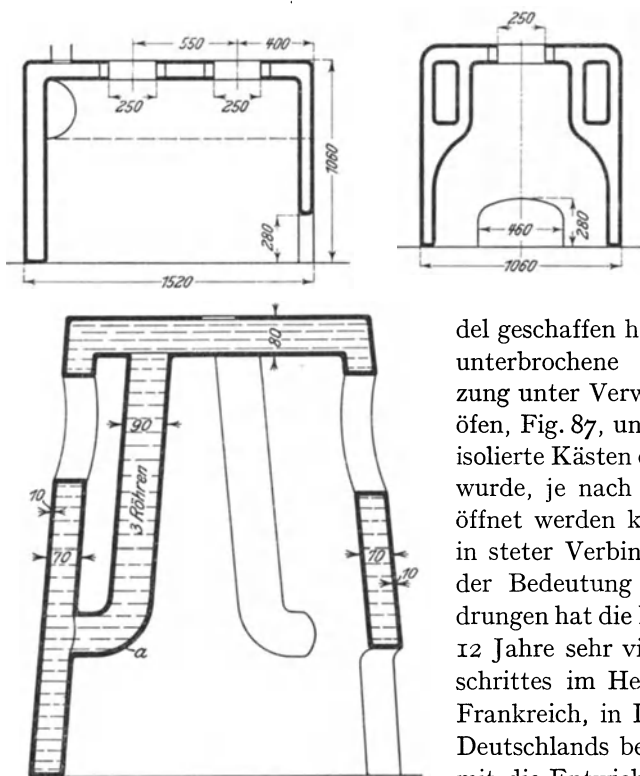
bis 90. Geschweißte Heizkessel.
